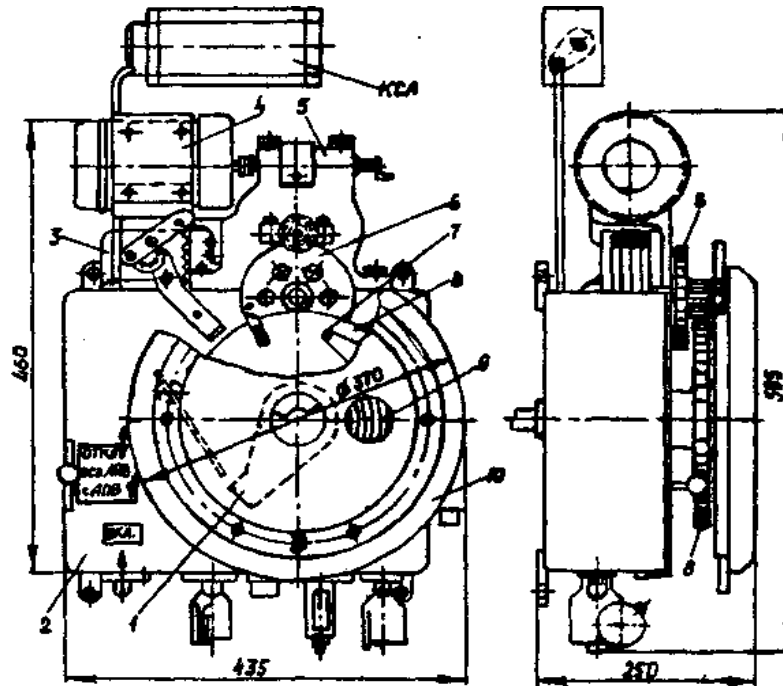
Пружинний привод з моторним редуктором ППМ-10:1 - заводний важіль; 2 - корпус; 3 - кінцевий вимикач; 4 - мотор; 5 - редуктор; 6 - велика шестірня зубчастої передачі; 7 - ролик ведучої собачки; 8 - шестірня взводу; 9 - спіральна пружина; 10 - штурвал
